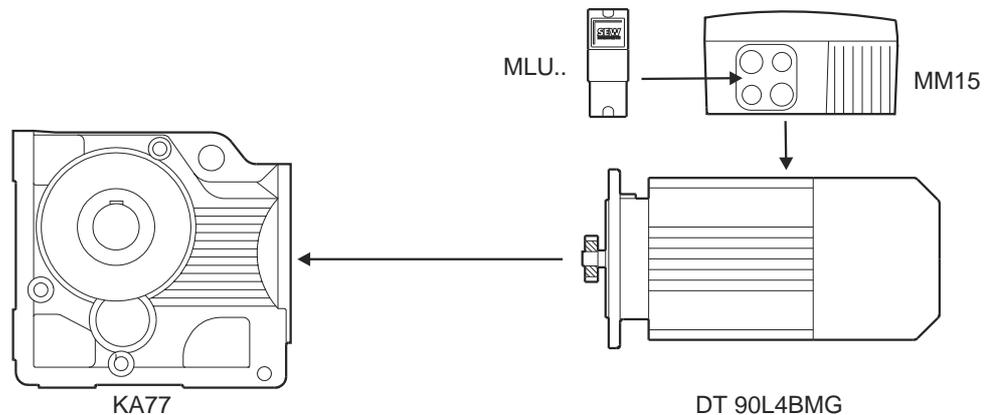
Beispiel für die Typenbezeichnung MOVIMOT®-Getriebemotor
